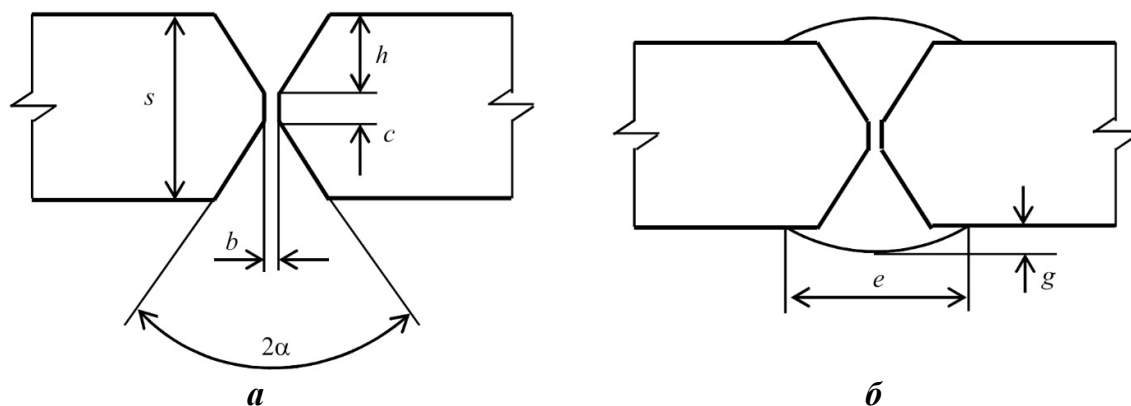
Конструктивні елементи стикового зварного з'єднання високоміцної сталі: *а* - підготовка кромek; *б* - заварений шов
